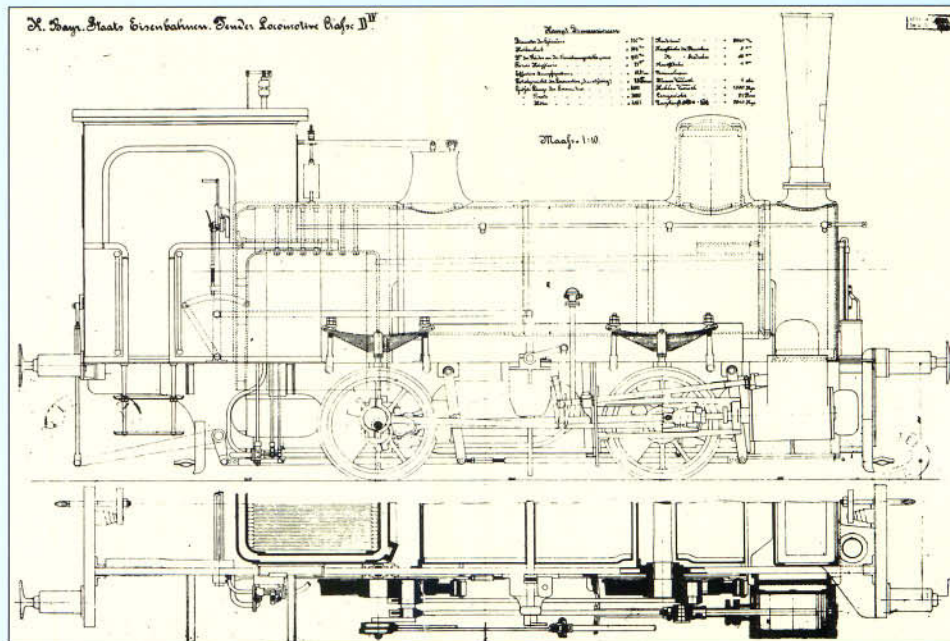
Seitenansicht und Grundriß aus der Hauptzeichnung 1:10.
